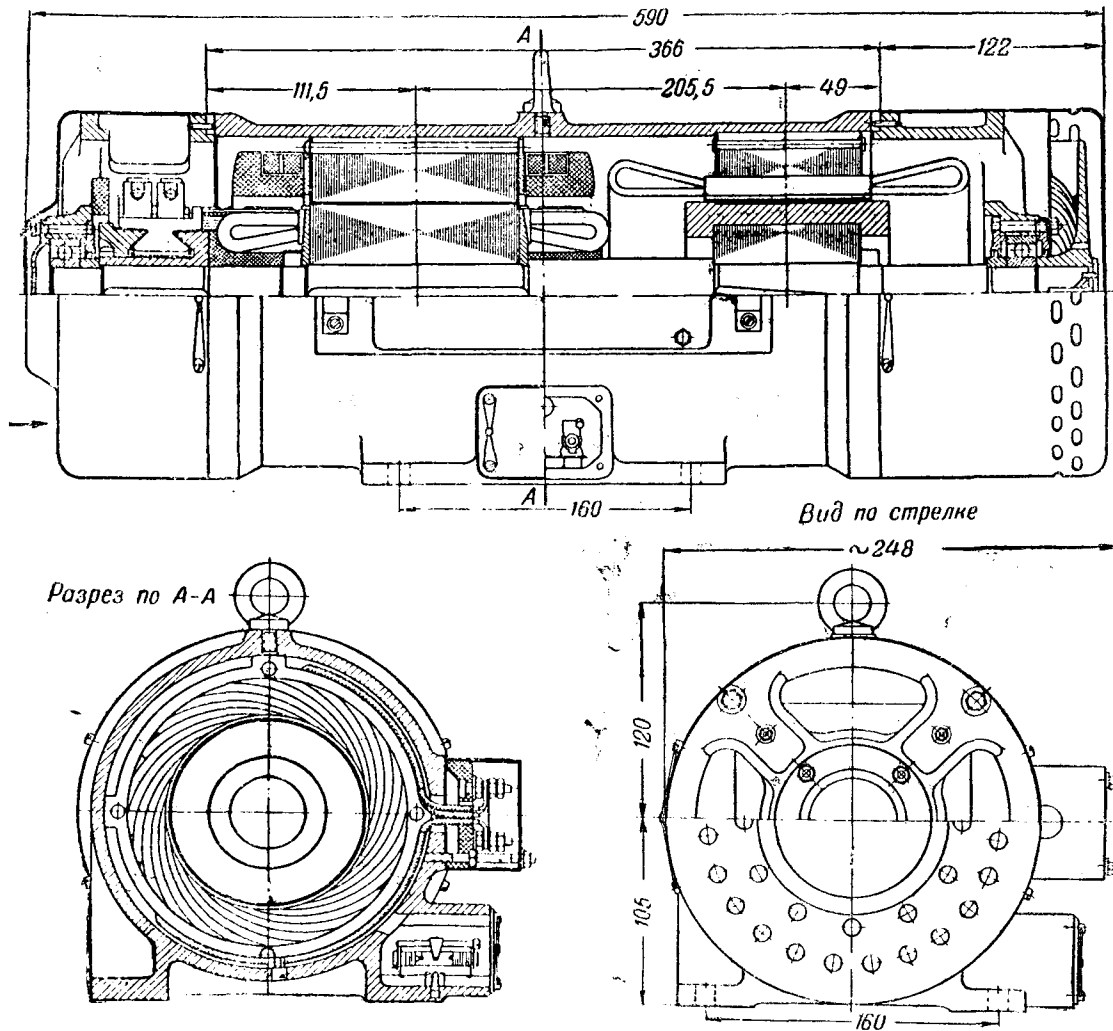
Типовая конструкция однокорпусного усилителя ВЭИ.
